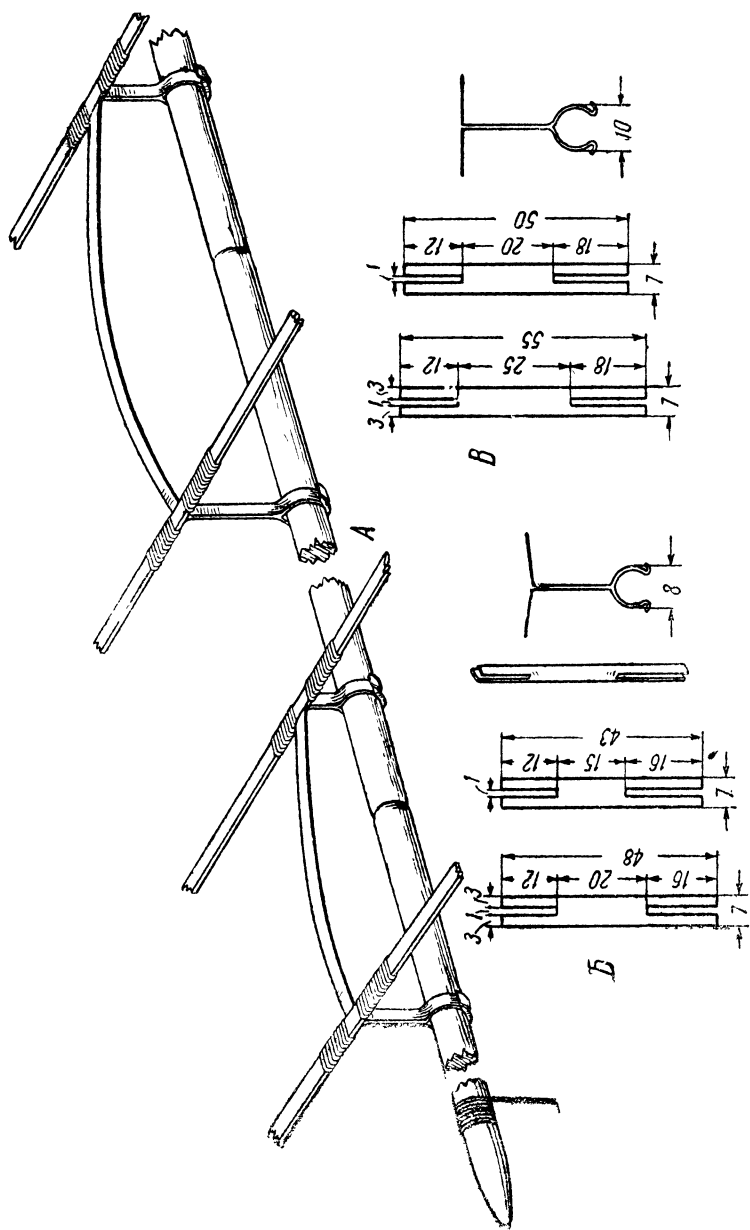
Крепление крыла и стабилизатора: А — общий вид крепления; Б — рабочие развертки подкосов и стабилизатора; В — рабочие развертки подкосов крыла
